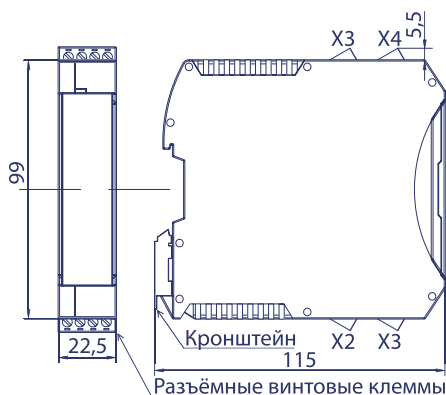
Габаритные размеры и крепление к DIN-рельсу
